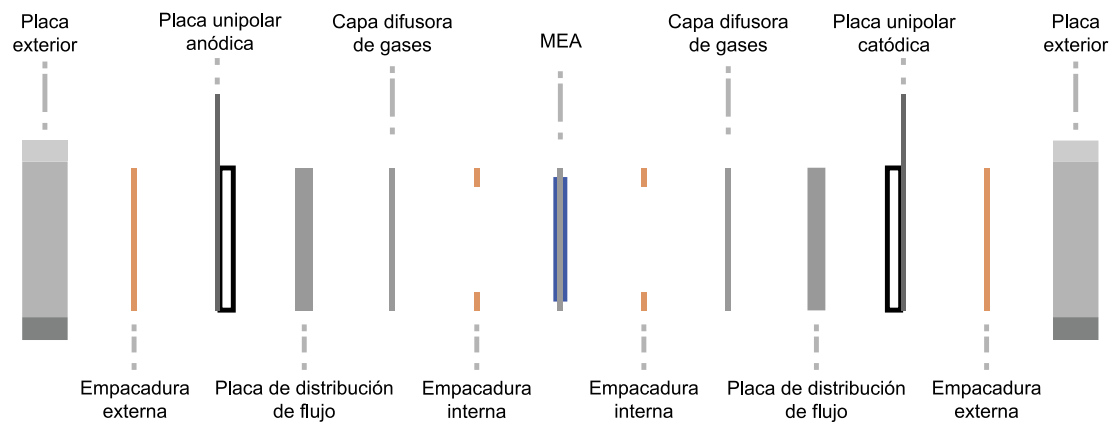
Diagrama explosionado de una celda PEM genérica.
